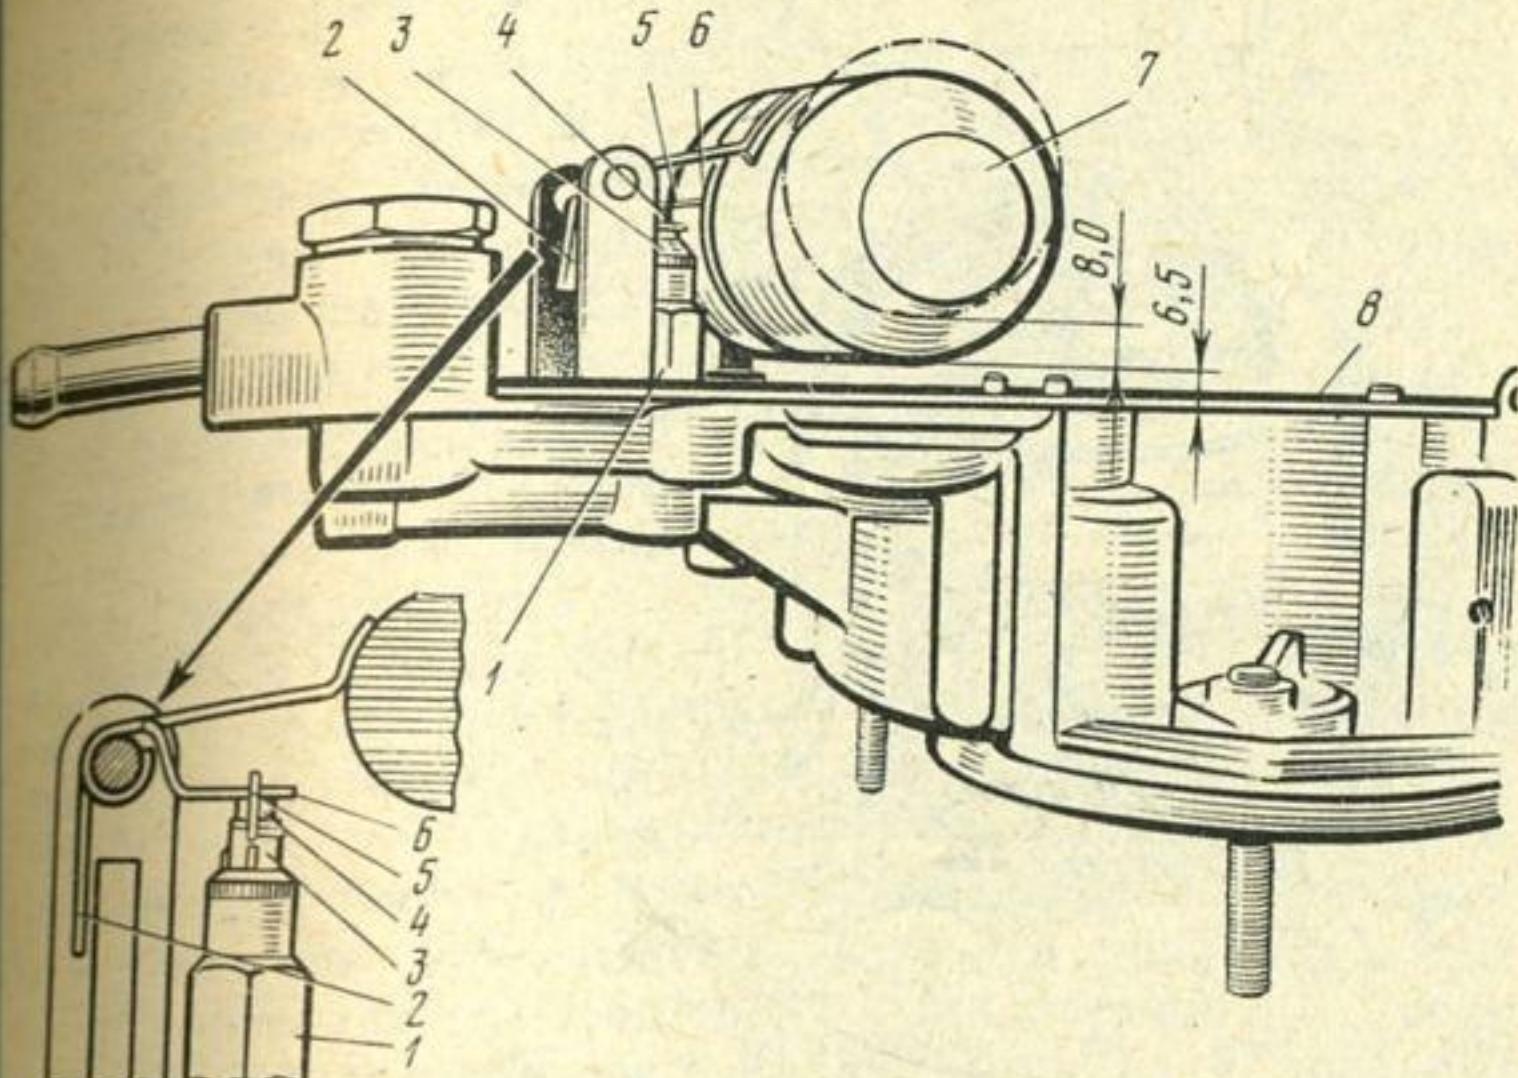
Регулирование положения поплавка на крышке поплавковой камеры карбюратора 2101-1107010-11:
